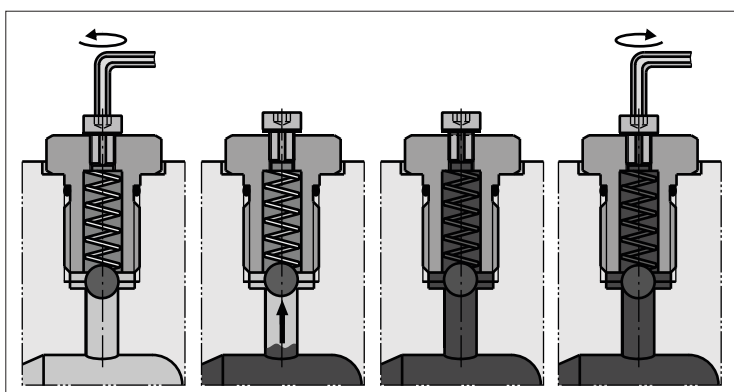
Hydraulikzylinder mit Rückschlagventil befüllen und entlüften
